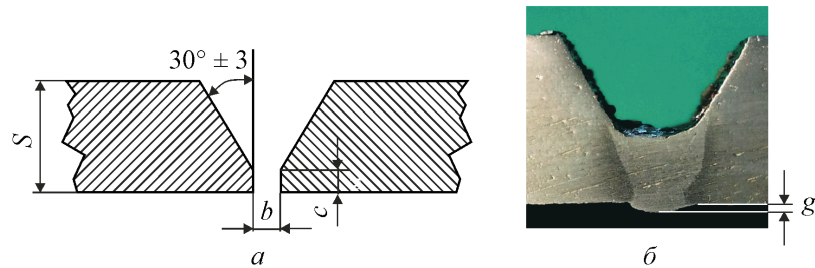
Подготовка кромок свариваемых труб для соединения типа С17 (а) и макрошлиф корневого шва (б): S — толщина трубы; b — зазор; c — притупление кромок; g — высота выпуклости обратного валика
